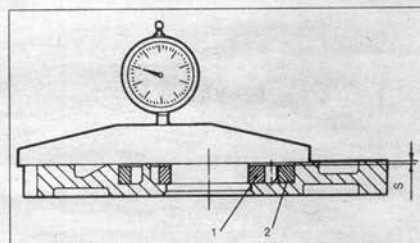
Замер осевых зазоров шестерен масляного насоса: 1 – ведущая шестерня; 2 – ведомая шестерня; s – осевой зазор
